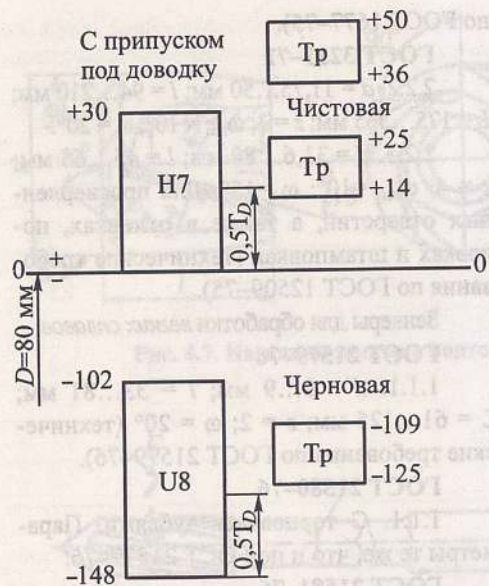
Схема расположения полей допусков отверстия диаметром 80Н7 и развертки для его обработки
